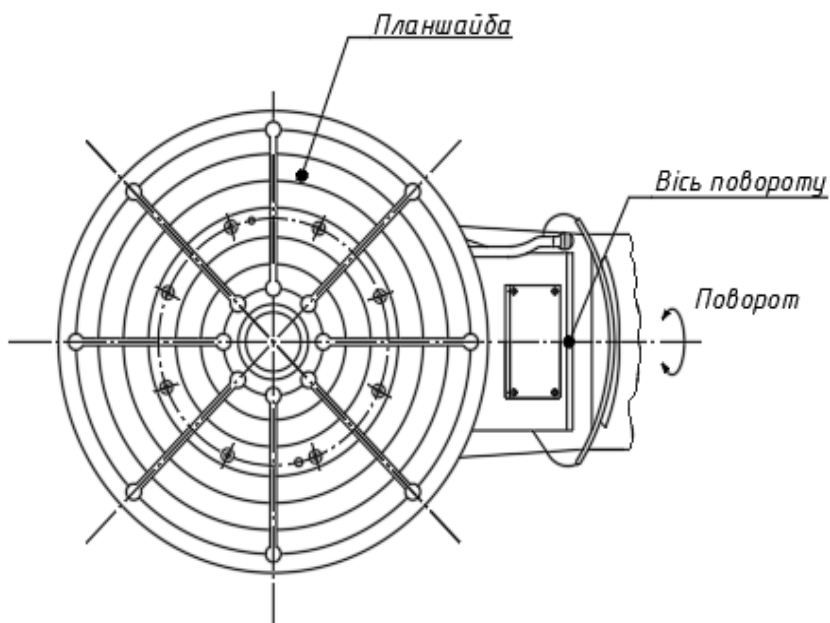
Блок обертальний УОПЗП (вид зверху)
